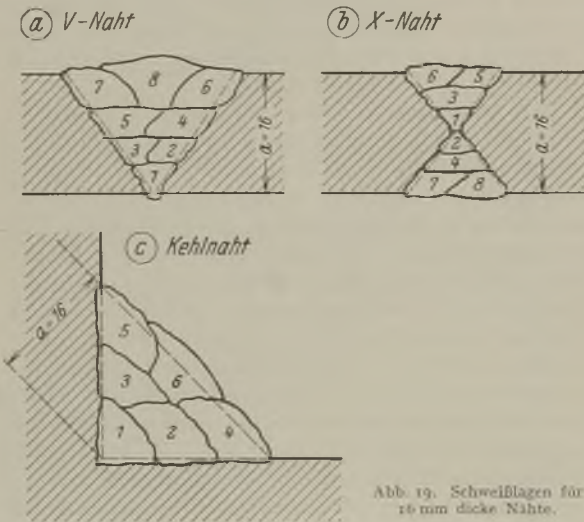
Schweißlagen für 16 mm dicke Nähte.
